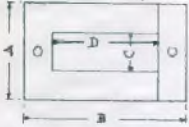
Das Maß-Schema für die Bleche unserer vier Drosseln.
